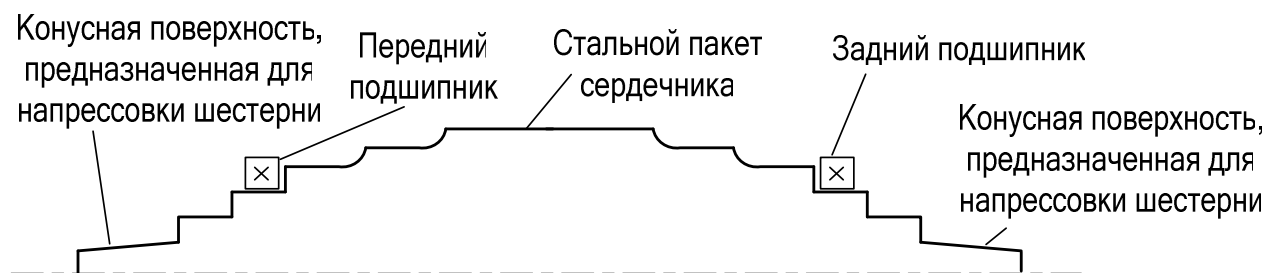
Схематичное изображение вала тягового двигателя
